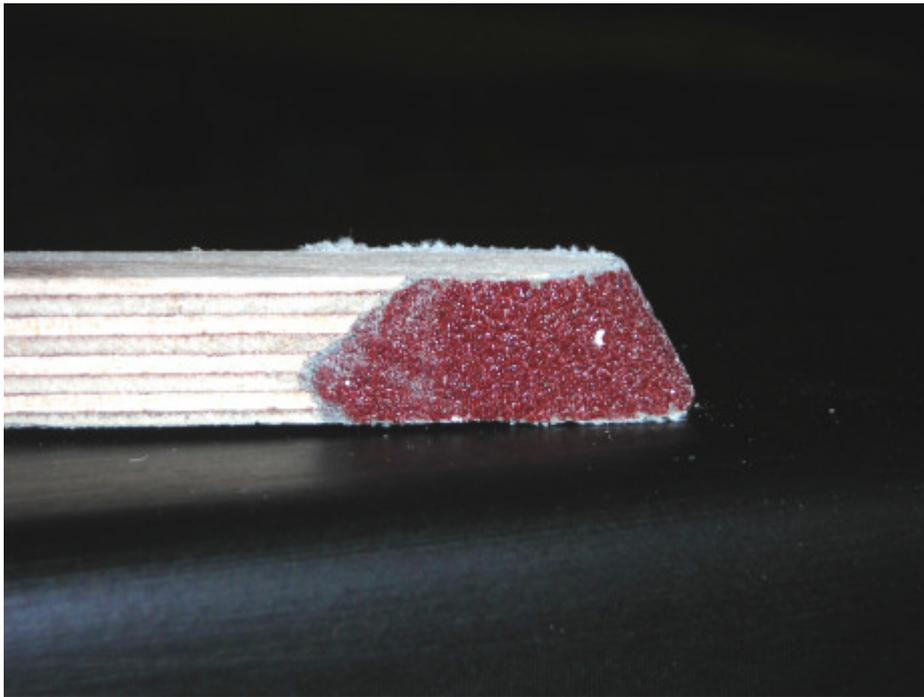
Abgeschrägte und verrundete Vierkantholzleiste, mit Schleifpapier beklebt
